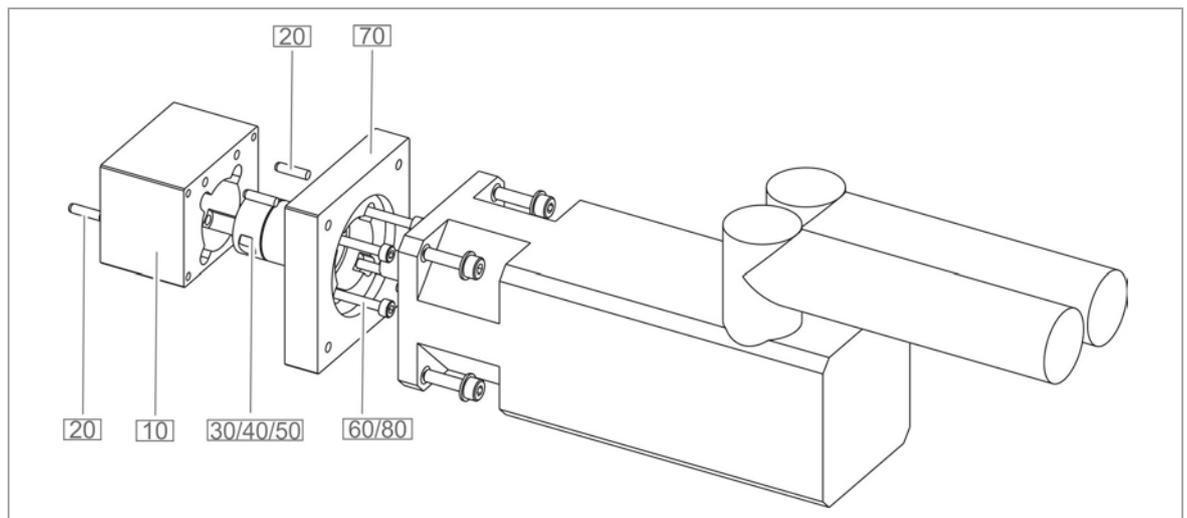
Flansch für axialen Motoranbau Lochkreis 63, 66 und 67, Explosionsdarstellung
